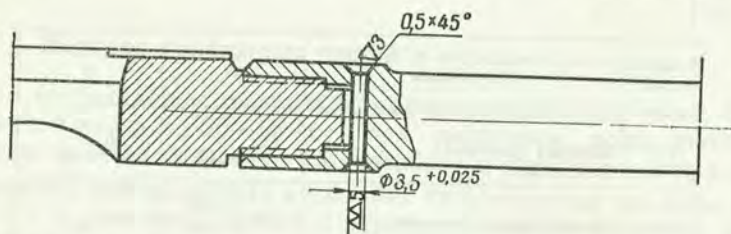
Обработка отверстия в газовом поршне и затворной раме
